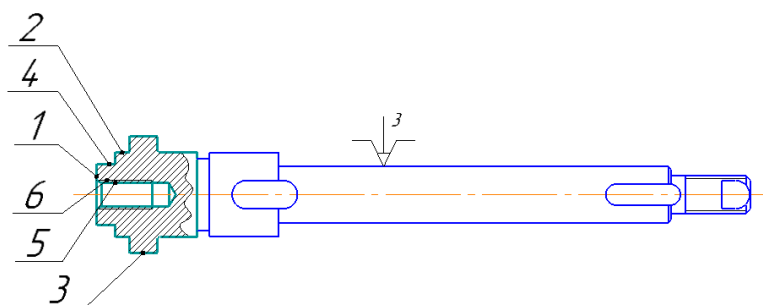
Эскиз обрабатываемой заготовки с пронумерованными поверхностями (установ Б)
